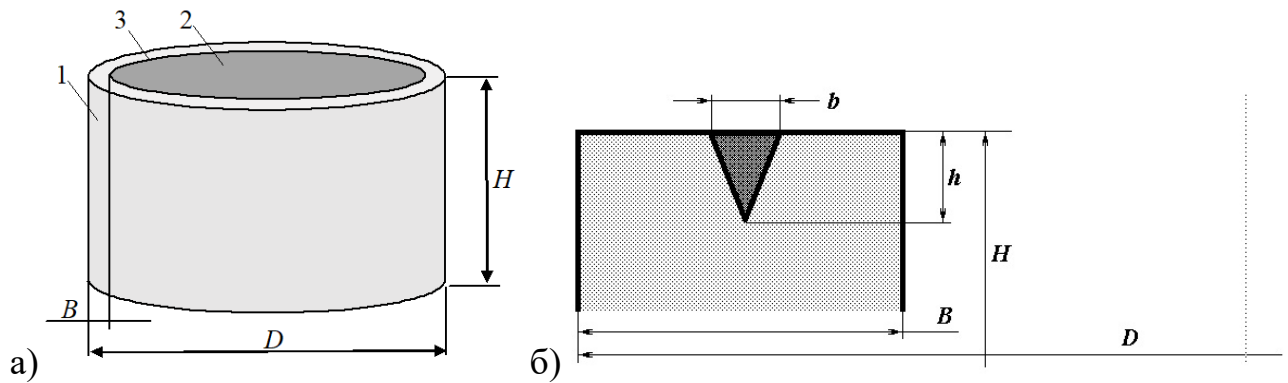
Геометричні параметри деталей, що зварюються, і лазерного провару (темна трикутна ділянка): 1 – корпус; 2 – фланець, що приварюється; 3 – зварний шов
